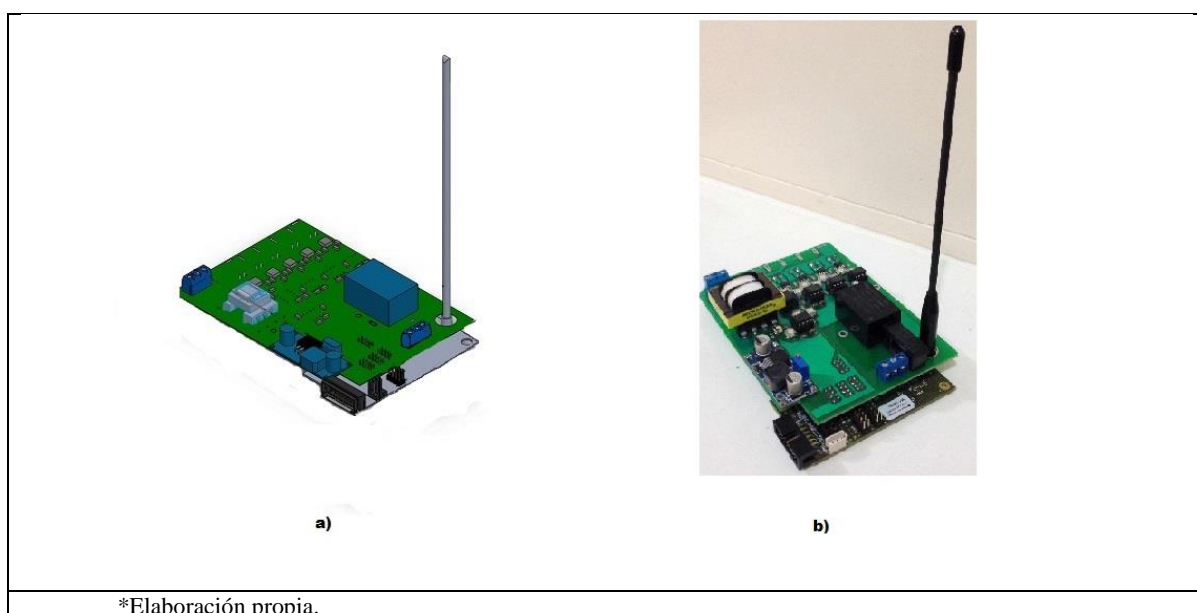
a) Modelo PCB + RF b) Estructura PCB + RF
